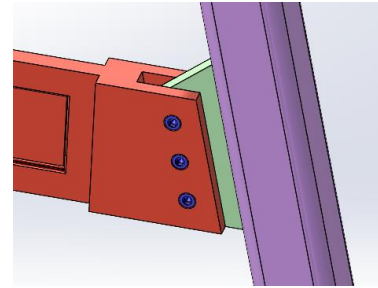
Detalle del sistema de amarre de las pletinas laterales a la estructura base (Fuente 20)
